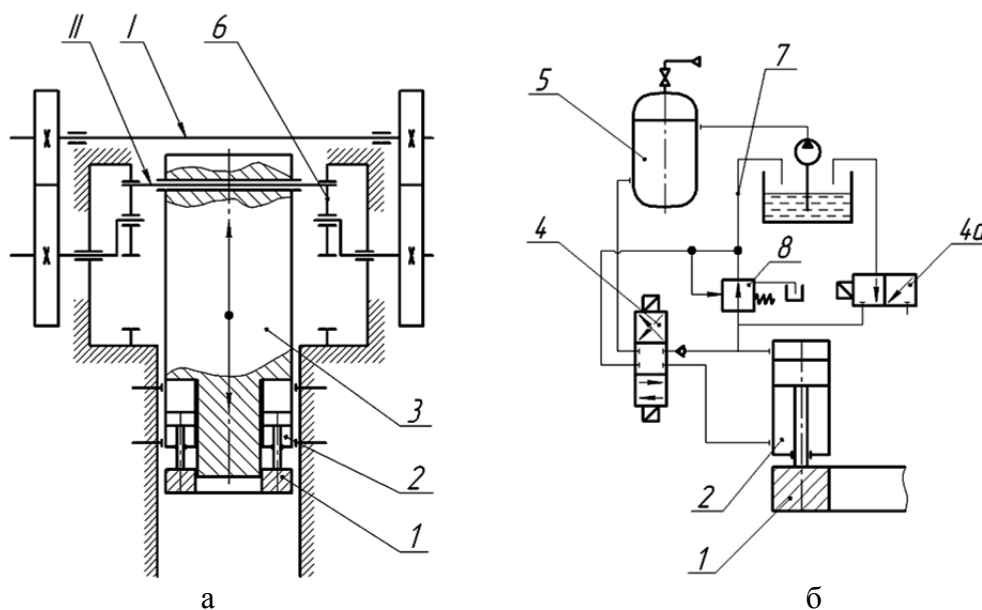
Кинематическая схема прессы двойного действия с бесшатунным главным исполнительным механизмом для глубокой вытяжки
